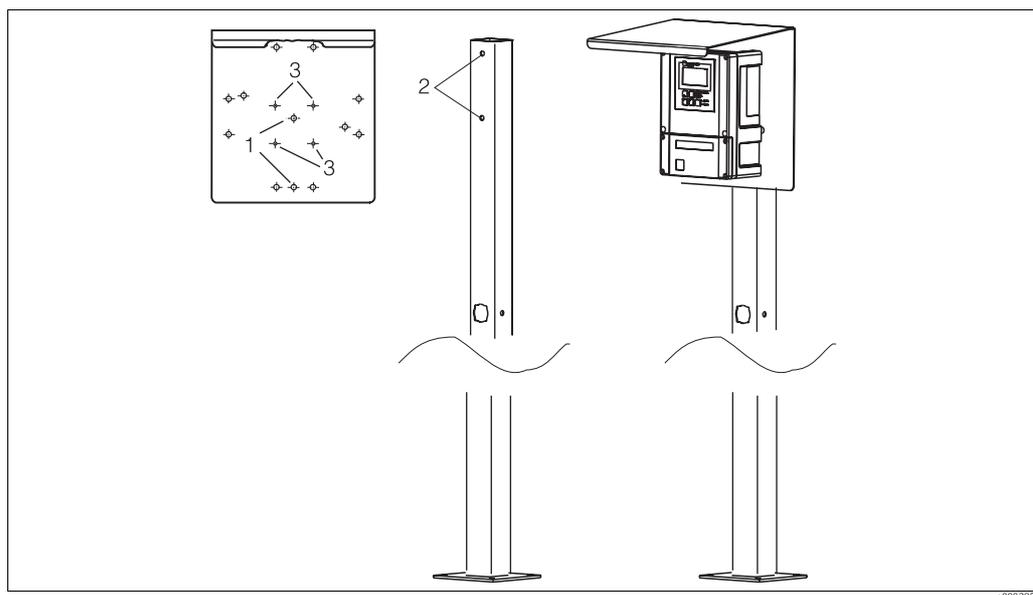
Montaggio del trasmettitore da campo su palina universale e con tettuccio di protezione dalle intemperie
